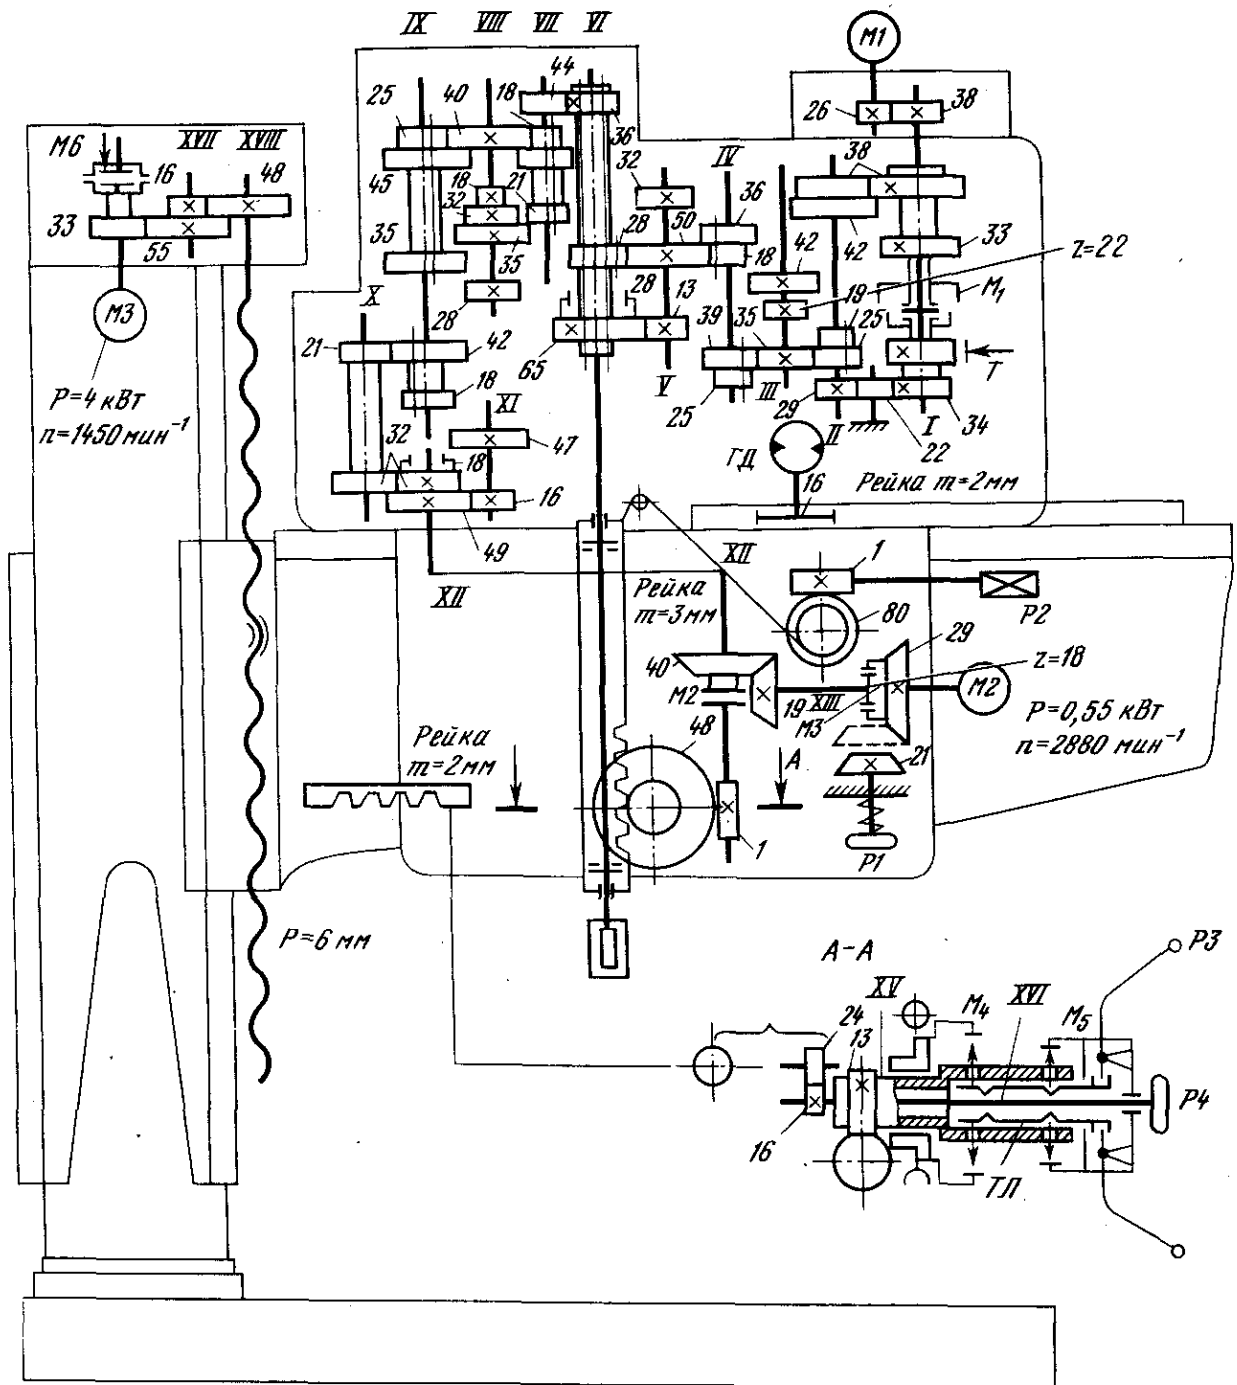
Кинематическая схема радиально-сверлильного станка
